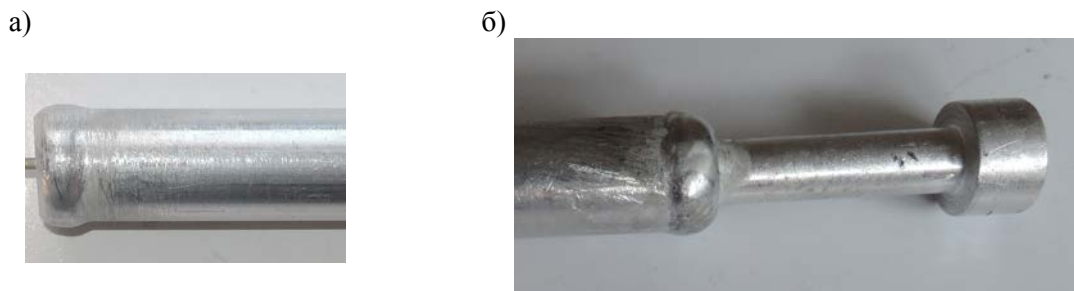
Внешний вид сварных швов в зоне герметизации ТТ со стороны доньшка-заглушки (а) и со стороны доньшка с заправочной трубкой (б)
